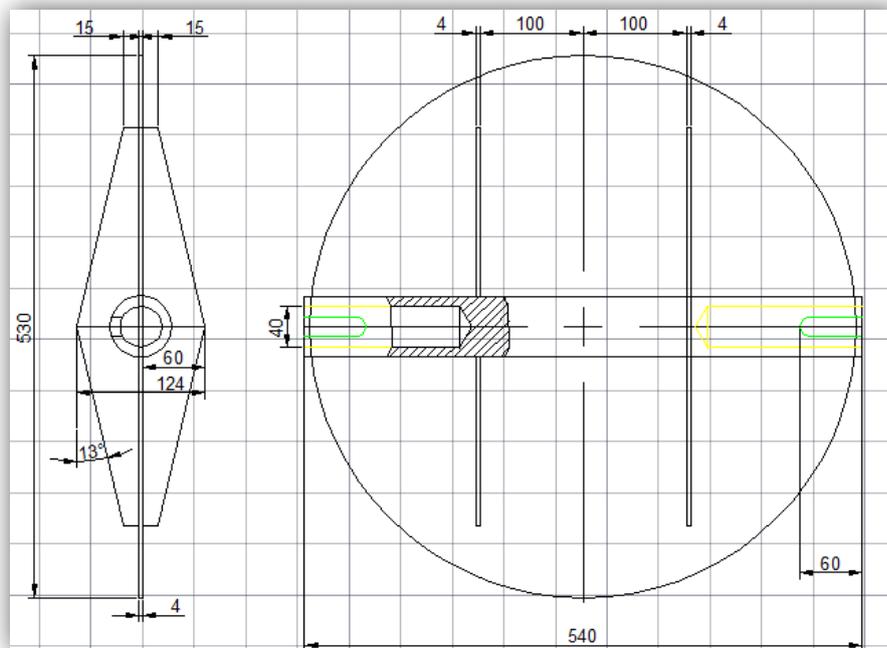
Dimensiones Dämper Horno de Fundición de Aluminio Fuente Planos Mecánicos CEDAL
